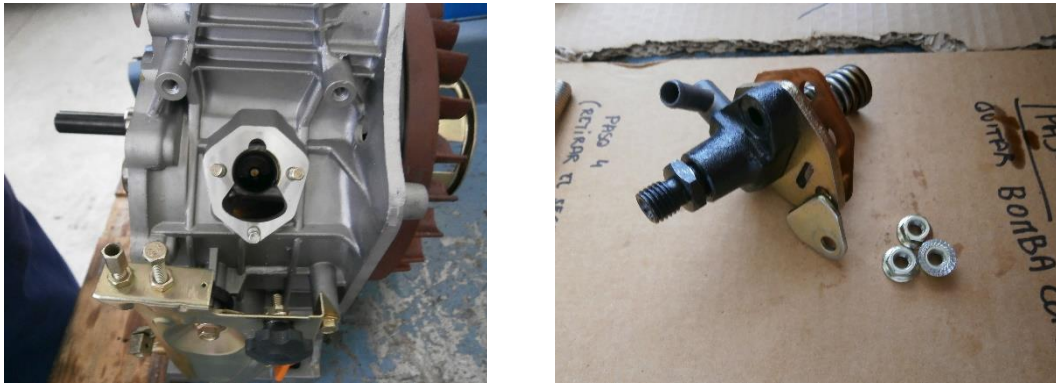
a) Con bomba de inyección de combustible y b) sin bomba.
